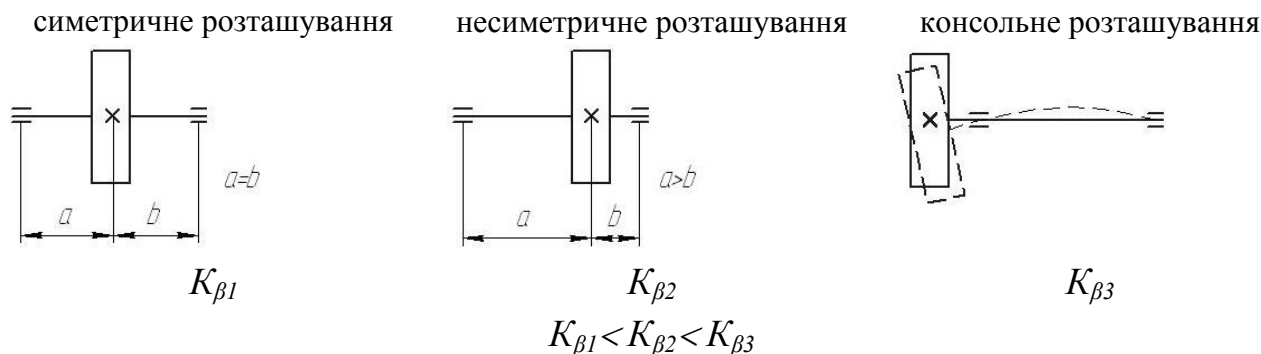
Схеми розташування зубчатих коліс на валах відносно опор
